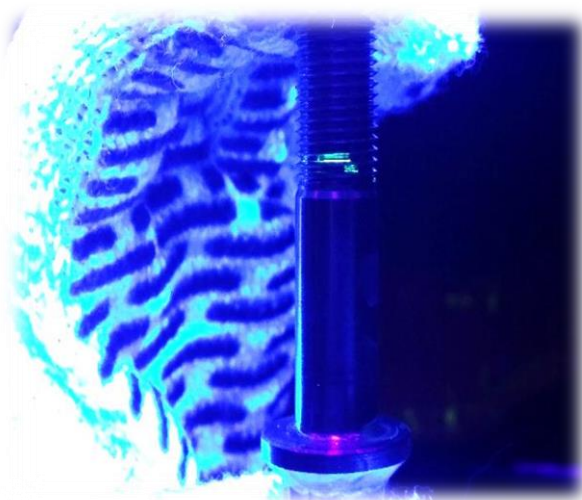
Трещина в 3-й резьбе болта чертежный номер 43-1389, выявленная флуоресцентным капиллярным методом неразрушающего контроля [10]
